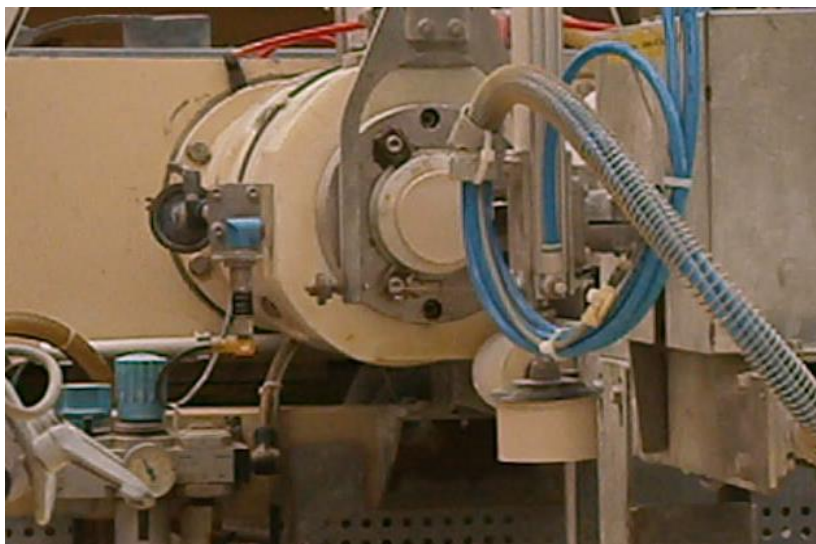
Corte da porção de pasta necessária para a contramoldagem.
